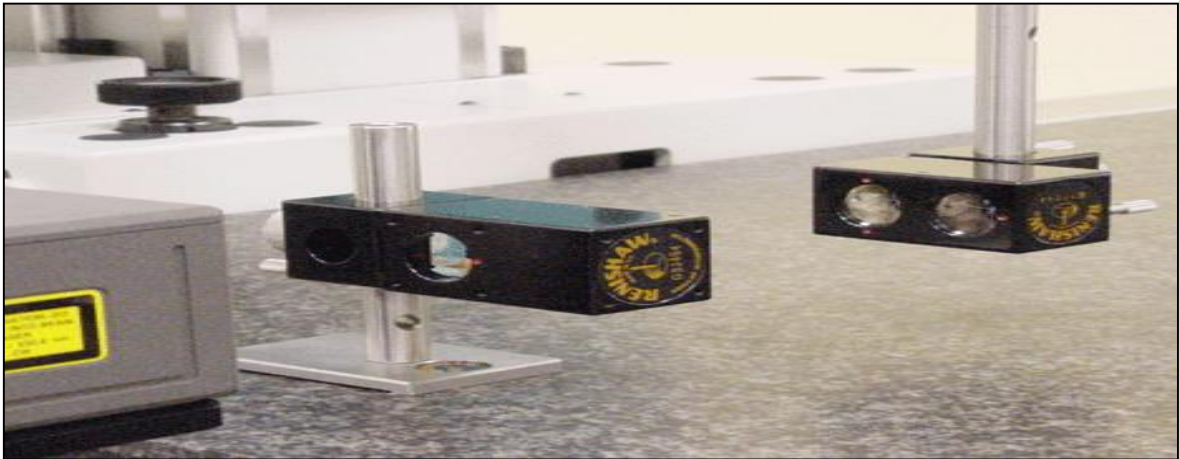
Optique angulaire montée sur machine à mesurer tridimensionnelle.
